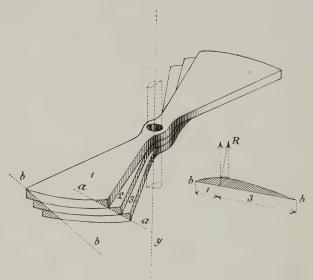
Construction d'une hélice en bois par collage de planches superposées. Les parties hachurées seront enlevées au cours de la construction, car l'hélice doit avoir la section figurée à côté. On voit, sur cette section, la direction R de la résistance de l'air et ses deux composantes : traînée et poussée.
